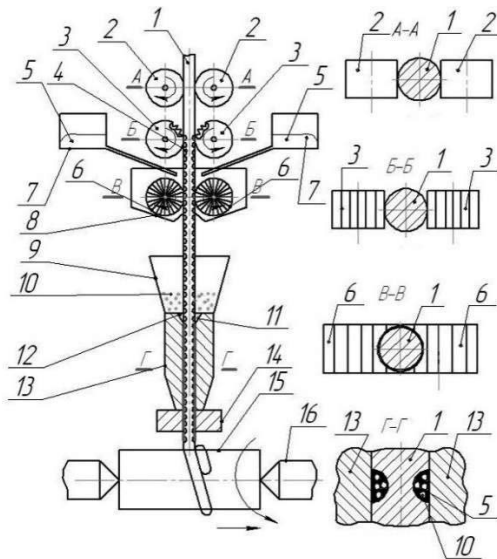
Конструктивна схема механізованого відновлення та зміцнення деталей: *A-A* – розріз конструктивної схеми калібрування зварювального дроту в напрямних роликах; *B-B* – розріз конструктивної схеми з насічками; *B-B* – розріз конструктивної схеми нанесення клейової речовини на зварювальний дріт; *Г-Г* – розріз конструктивної схеми ущільнення порошку з легуючими компонентами в насічках
